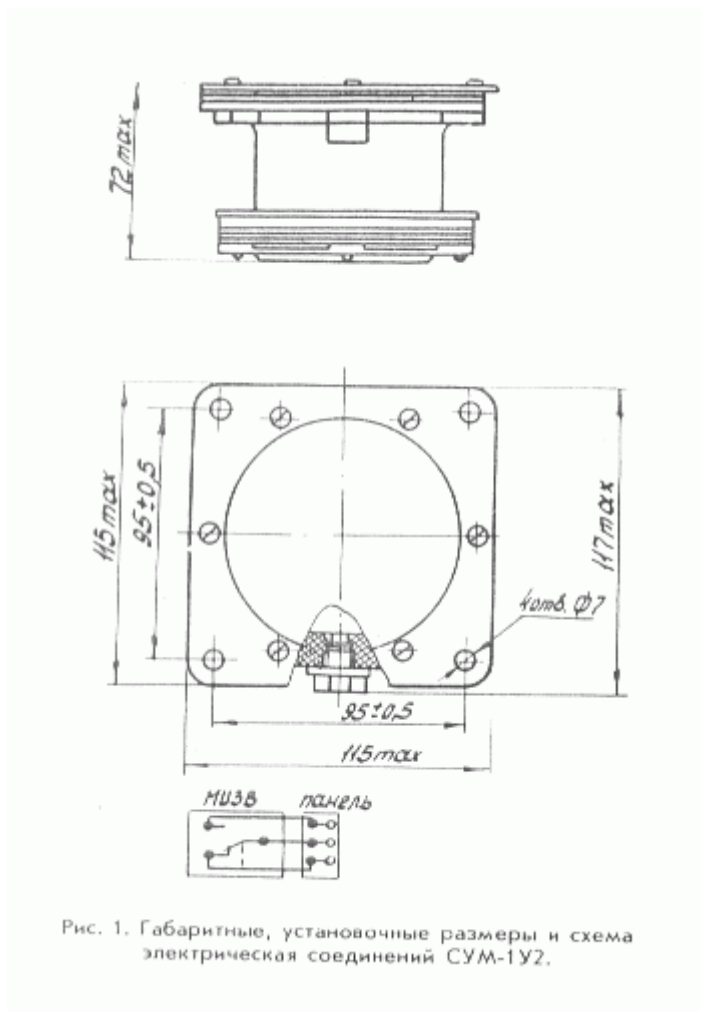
Габаритные, установочные размеры и схема электрической соединений СУМ-1У2.
